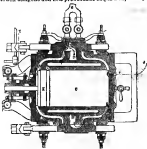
WINTON ENGINE, SECTION LONGITUDINALE.
